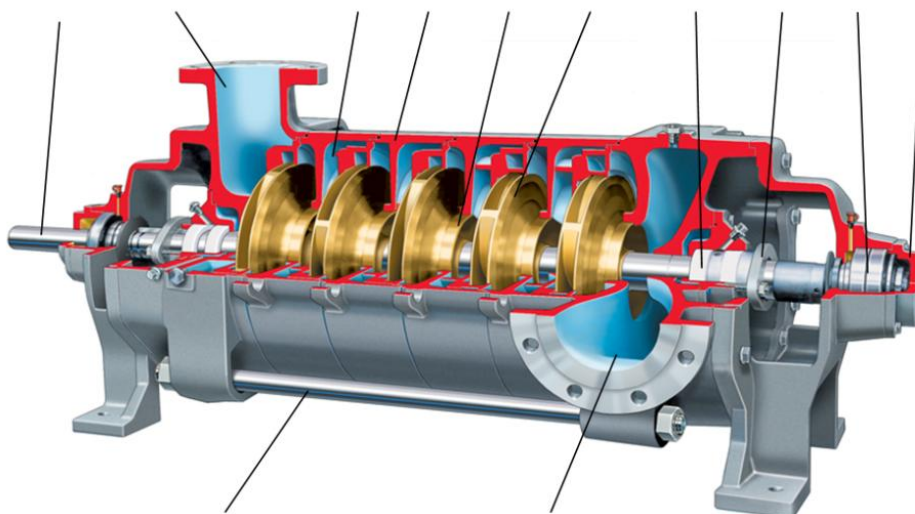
Центробежный многоступенчатый горизонтальный секционный насос типа ЦНС (МС):
